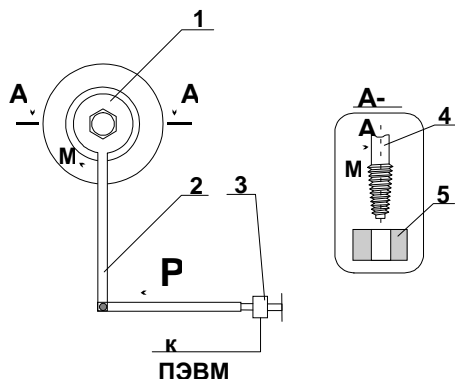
Схема испытаний процесса нарезания внутренней резьбы: 1 – приспособление, 2 – рычаг, 3 – датчик, 4 – инструмент, 5 – заготовка.
